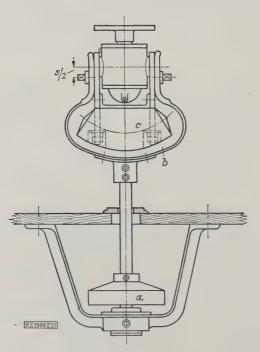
Antrieb eines Plansichters mit pendelndem Schwunggewicht.
